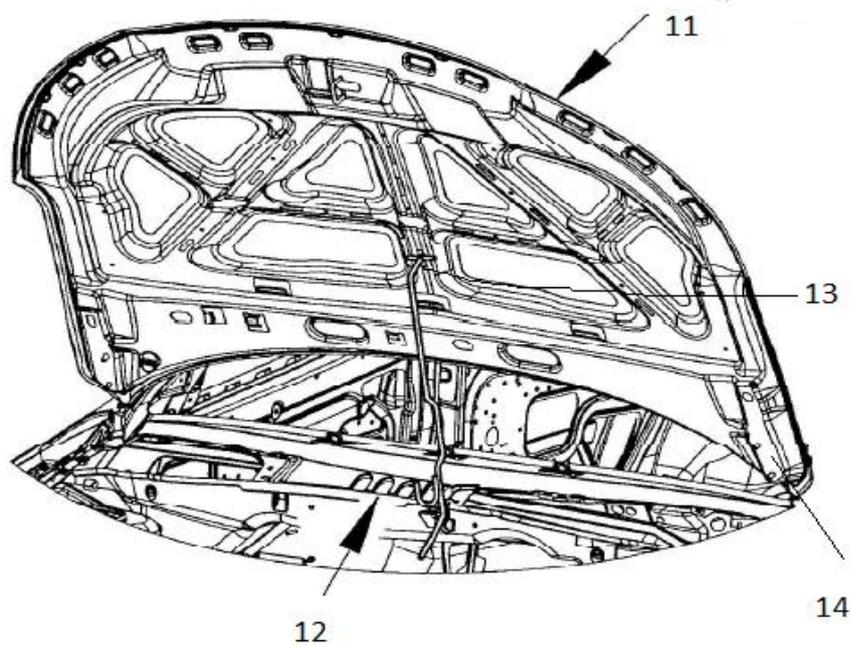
Поверхности установки оснастки крышка капота в сборке
